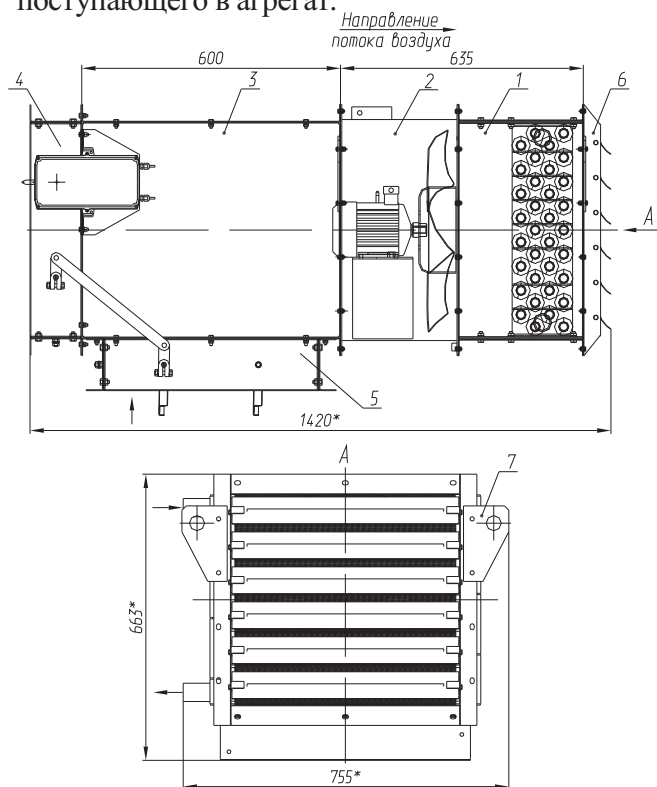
Габаритные, установочные и присоединительные размеры агрегата АО-ВВО-4 со смесительной камерой
